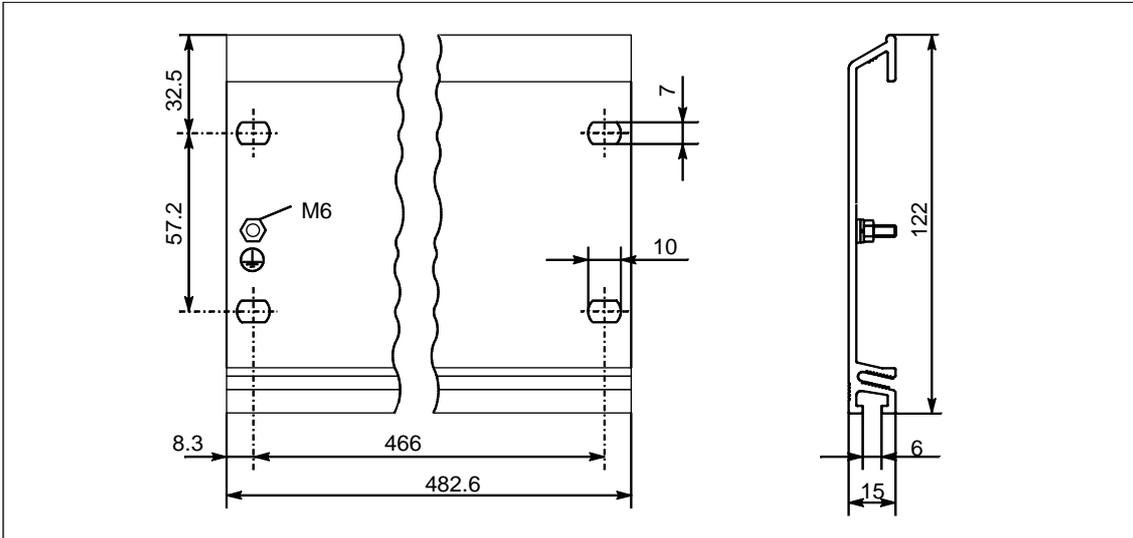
Чертеж с размерами профильной шины стандартной ширины 482,6 мм
